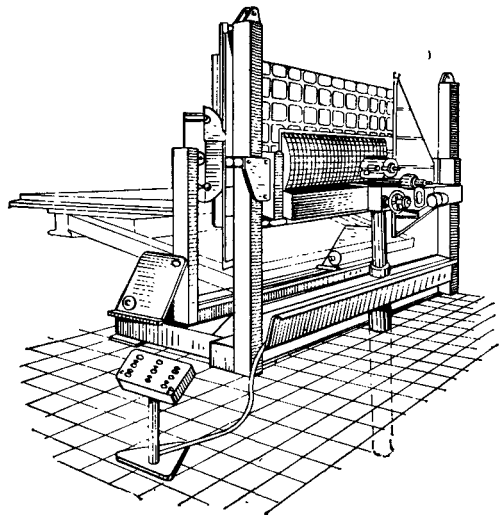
Копировально-фрезерный станок фирмы «Фоккер».
